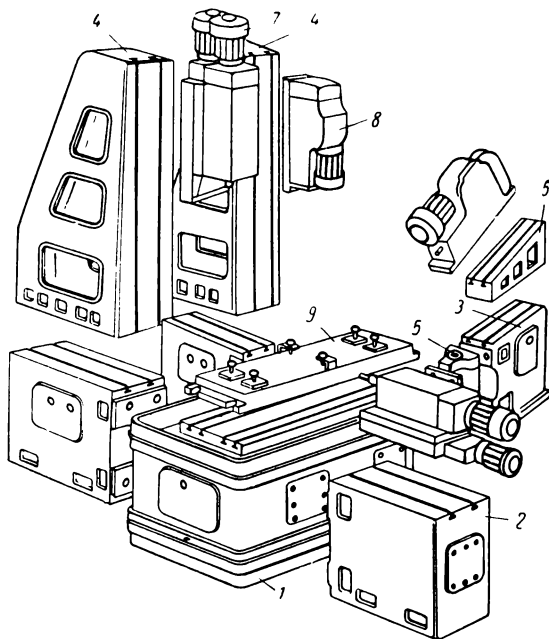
Агрегатный фрезерный станок с прямоугольным столом
